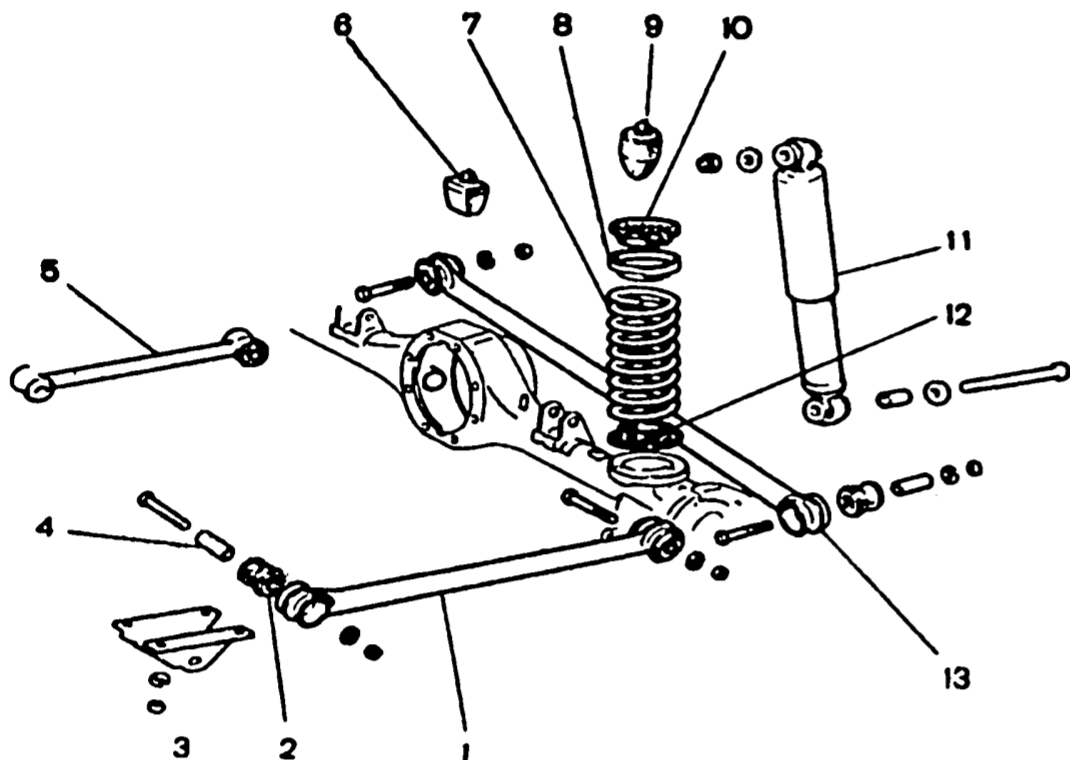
Детали задней подвески: 1 - нижняя продольная штанга; 2 - резиновая втулка; 3 - кронштейн крепления нижней продольной штанги к кузову; 4 - распорная втулка; 5 - верхняя продольная штанга; 6 - дополнительный буфер хода сжатия; 7 - пружина; 8 - верхняя чашка пружины; 9 - буфер хода сжатия; 10 - верхняя изолирующая прокладка пружины; 11 - амортизатор; 12 - нижняя изолирующая прокладка пружины; 13 - поперечная штанга
